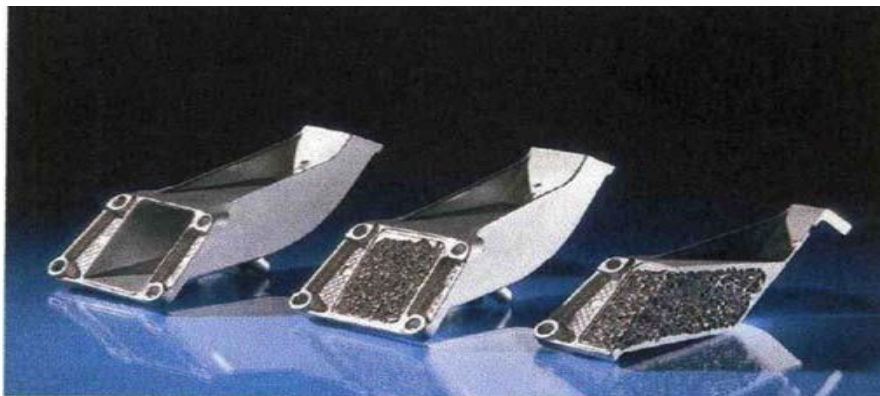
Prototype d'un support moteur BMW construit par LKRE (Ranshofen, Autriche).
